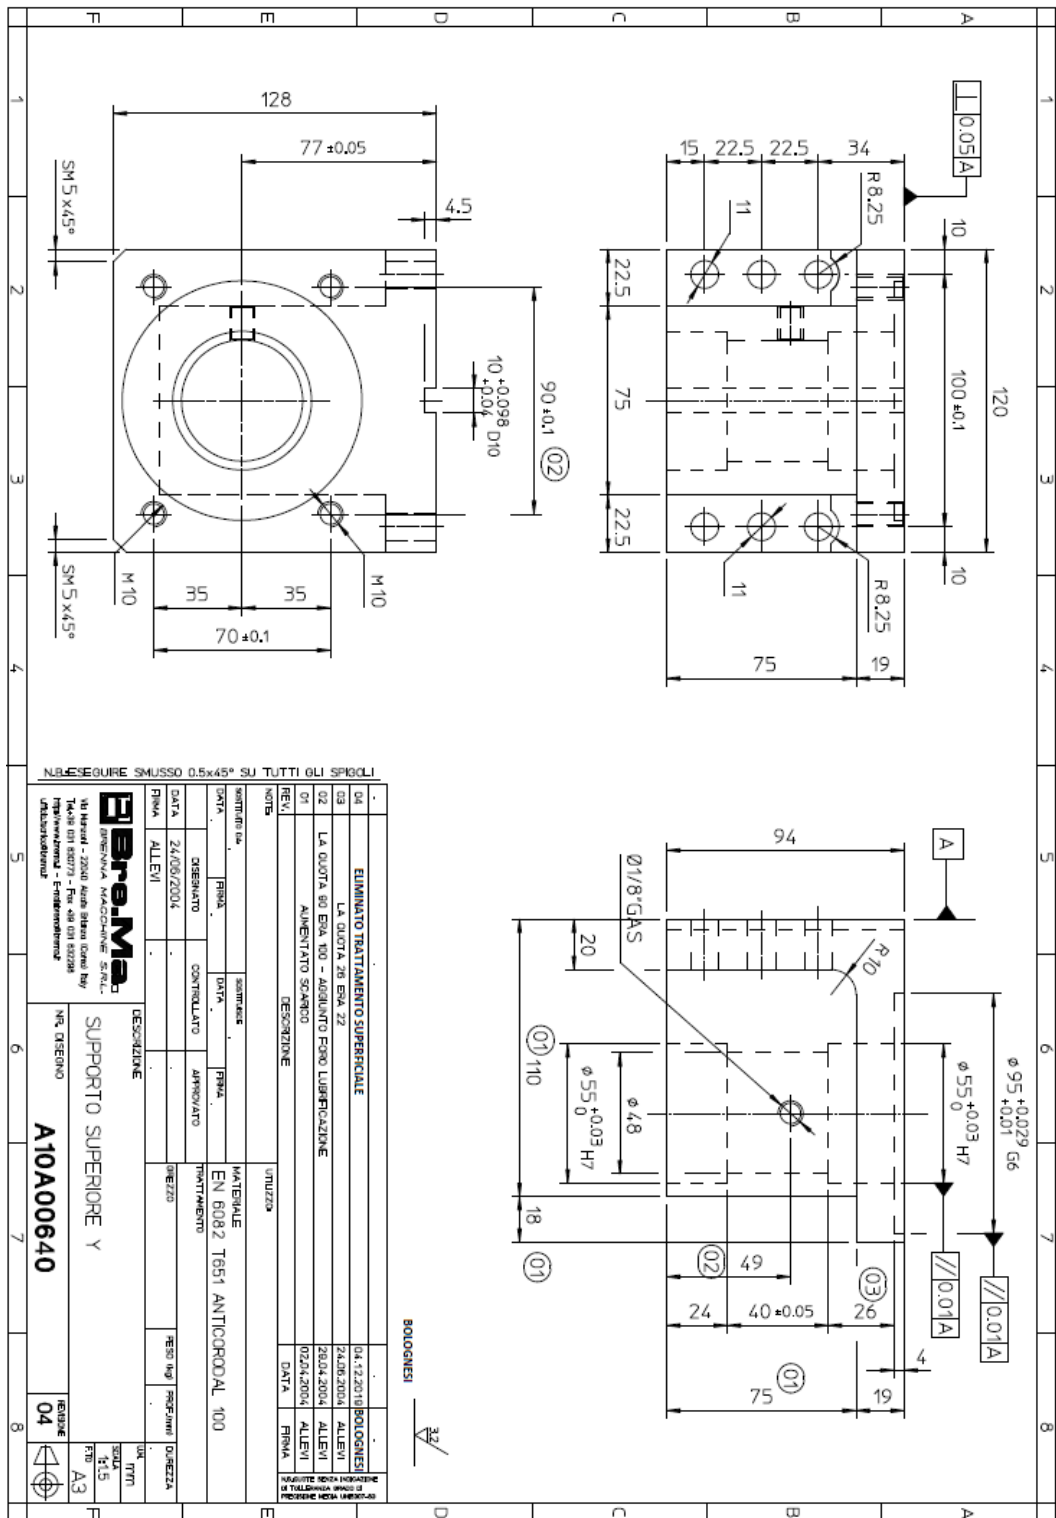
Disegno tecnico SUPPORTO SUPERIORE Y
